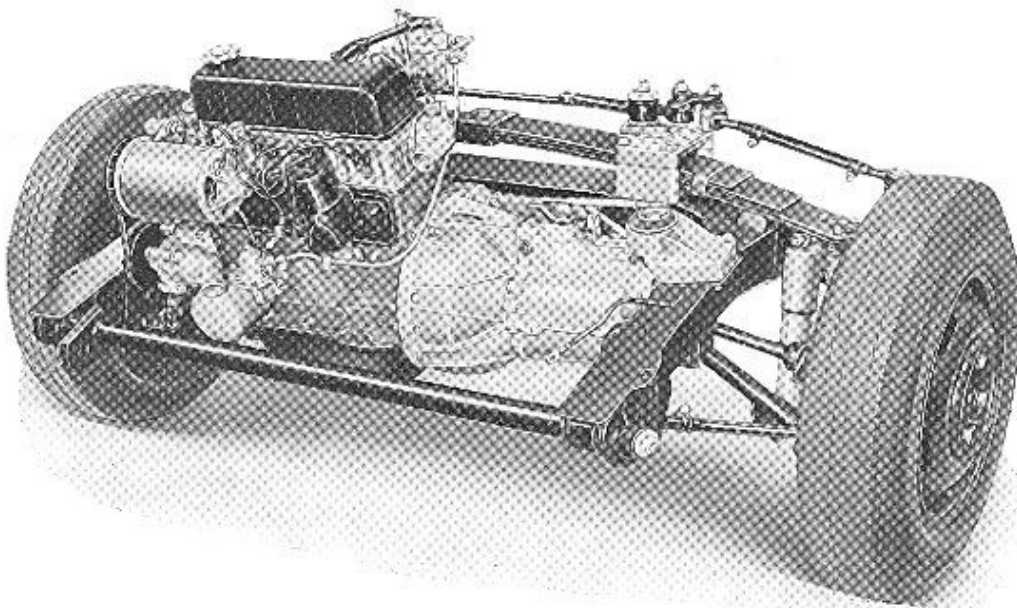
Linke Seitenansicht der Vorderrad- und Motoraufhängung.
